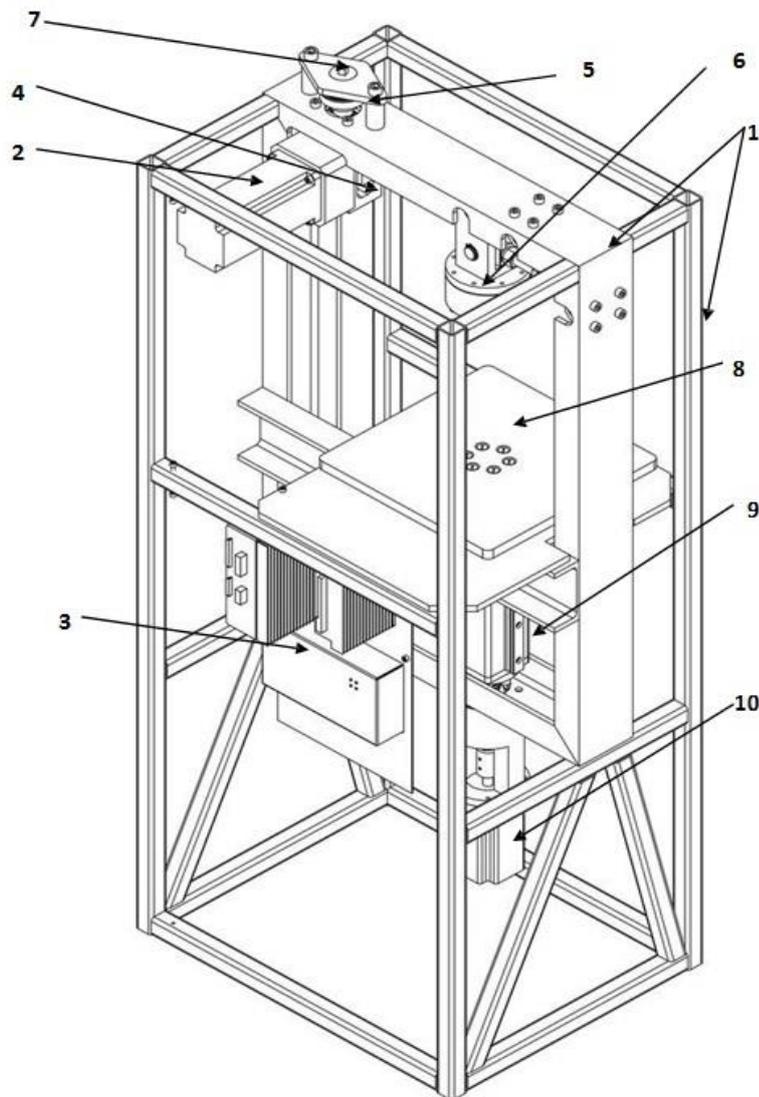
Вид ПДИ с указанием основных элементов: 1-рама; 2-сервопривод; 3 - блок электроники; 4-эксцентрик; 5-пружина; 6-датчик силы; совмещенный с толкателем; 7- натяжитель-фиксатор пружин; 8 - подъемный стол; 9- направляющие (линейные подшипники); 10-шаговый двигатель
